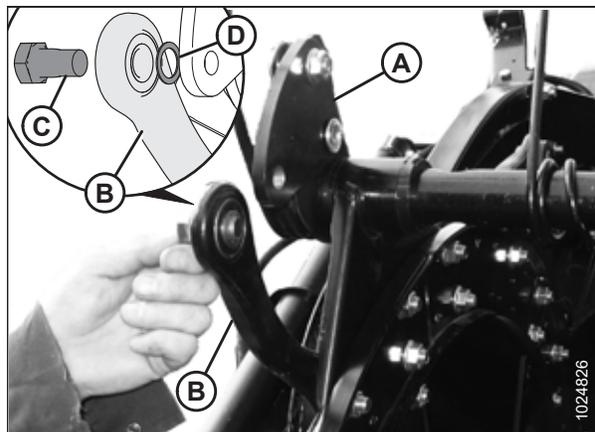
Trou de fixation du levier de la barre et alignement de la biellette
